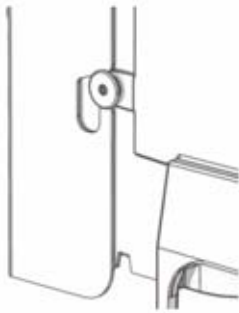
Einführung der Schrauben in die Führungsschlitze - Detailansicht
